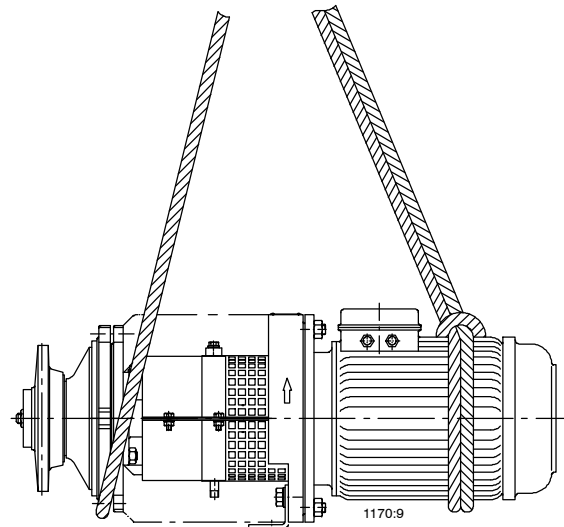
Транспортировка моноблочного насосного агрегата с двигателем
